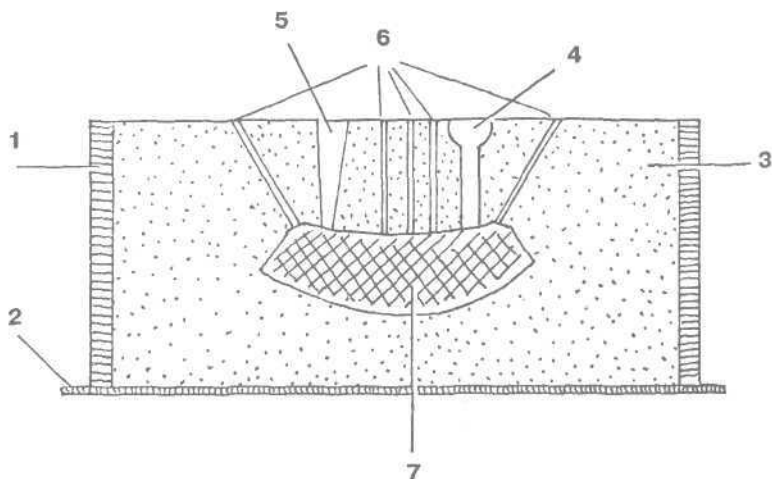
Изготовление модели: 1 — опока; 2 — подмодельная доска; 3 — формовочная смесь; 4 — литник; 5 — выпор; 6 — дополнительные отверстия; 7 — модель
